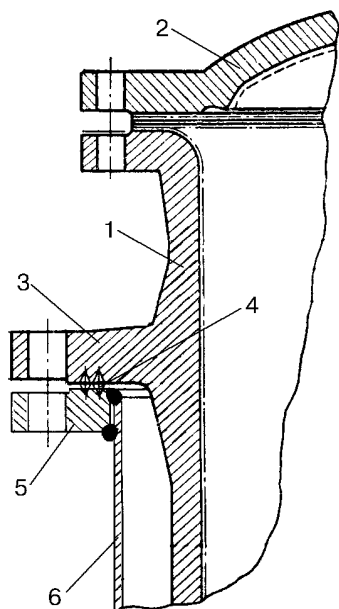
Конструкция разъемного крепления рубашки к корпусу аппарата:
